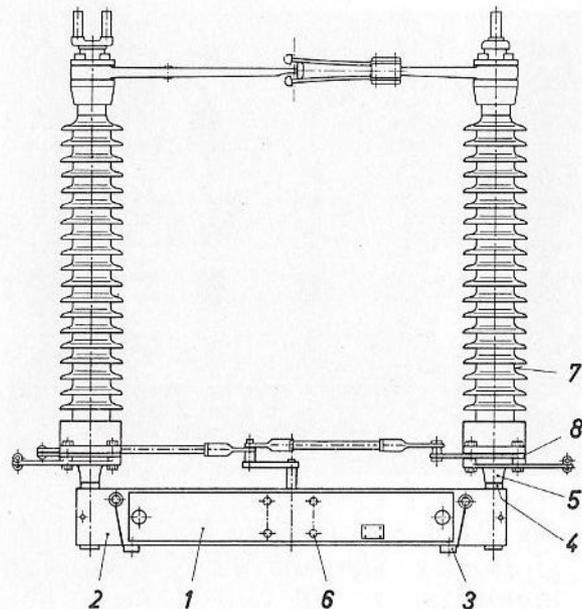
Disposición constructiva del seccionador de columnas giratorias Siemens: 1—Bastidor. 2—Placa de refuerzo. 3—Placa de apoyo. 4—Cubo. 5—Brida giratoria. 6—Taladro de fijación. 7—Columna giratoria aislante. 8—Palanca de acoplamiento.
